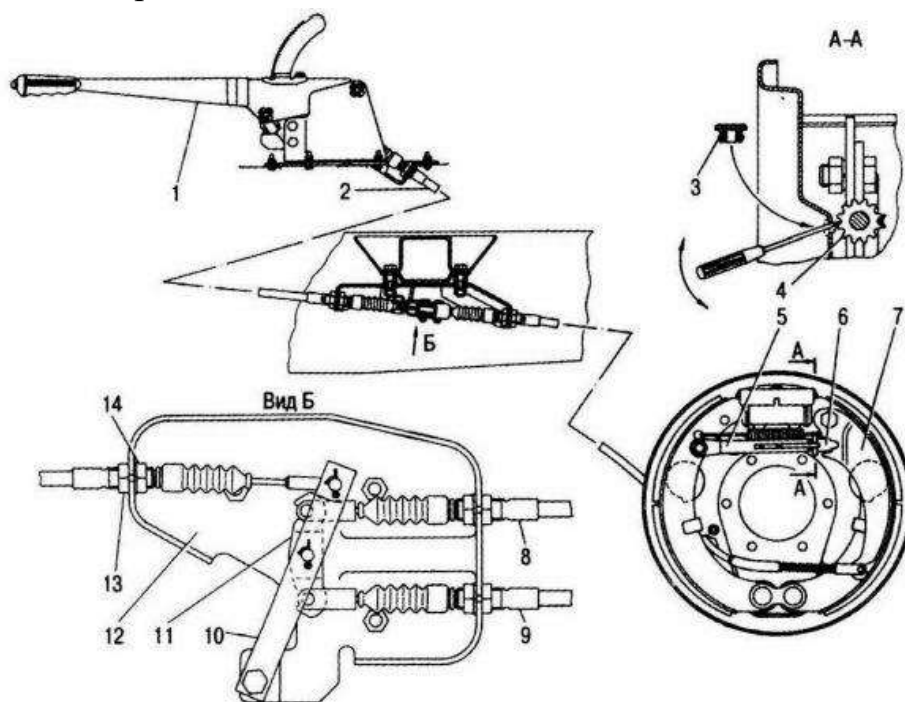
Стояночная тормозная система: 1 – рычаг; 2 – передний трос; 3 – заглушка; 4 – регулировочный винт; 5 – разжимное звено; 6 – опорная втулка; 7 – рычаг привода; 8, 9 – задние тросы; 10 – рычаг уравнивателя; 11 – уравниватель; 12 – кронштейн; 13 – регулировочная гайка; 14 – контргайка
